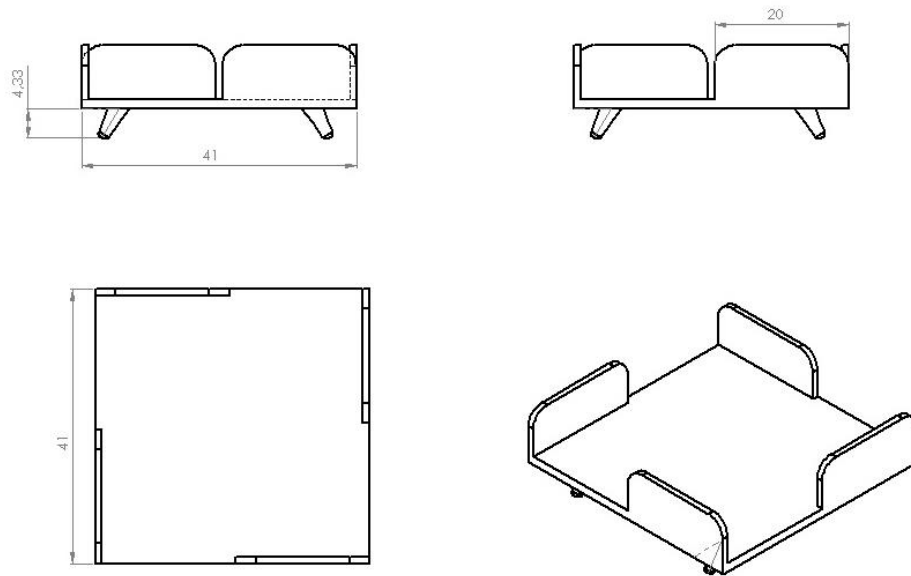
Desenho técnico CAD 3D da opção I (Fonte: Autor)
